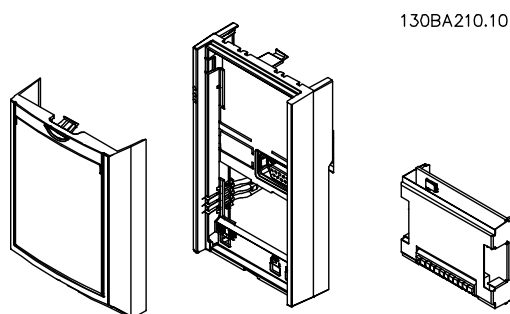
Детали для версий с покрытием/без покрытия
